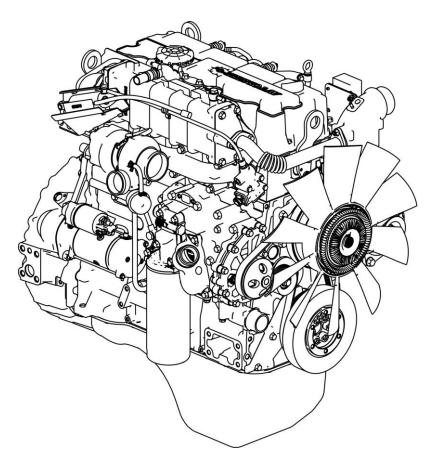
Двигатель ЯМЗ-53443-21 (общий вид справа)
